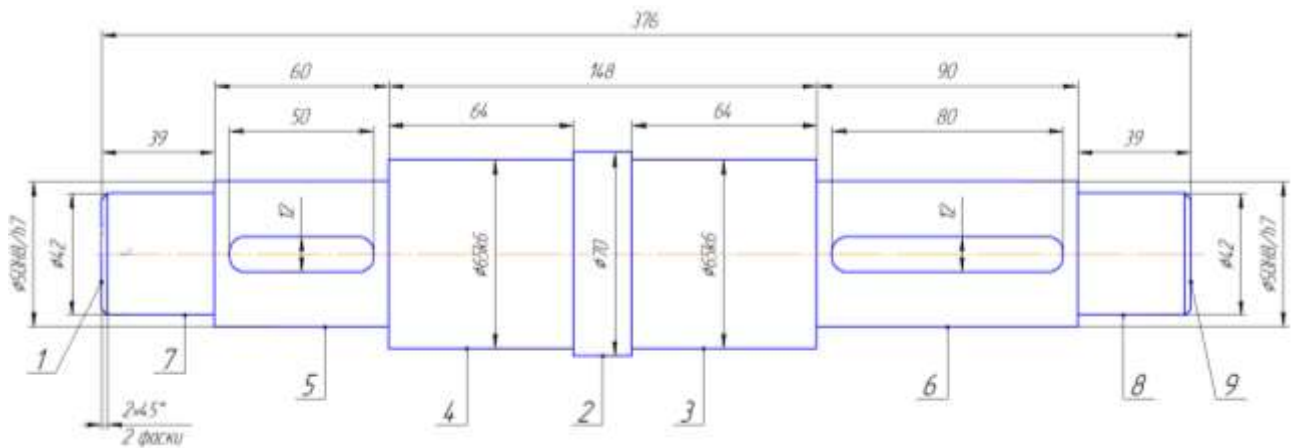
Розбивка деталі на елементарні поверхні
